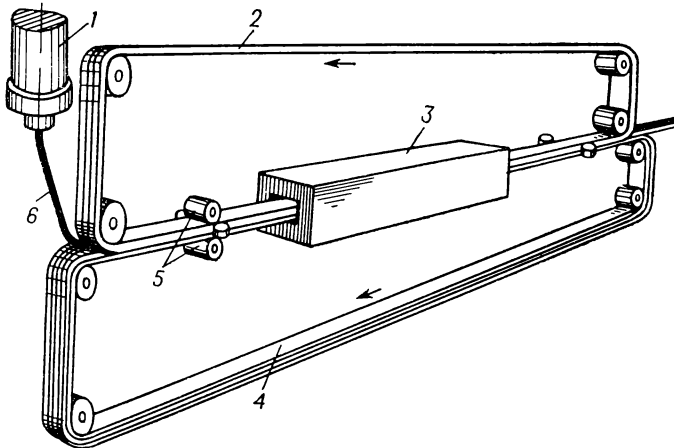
Способ непрерывной вулканизации профилей: 1 — головка шприц-машины; 2—4 — эластичные ленты полуформы; 3 — обогреваемая камера; 5 — прижимные валки; 6 — изделие.
